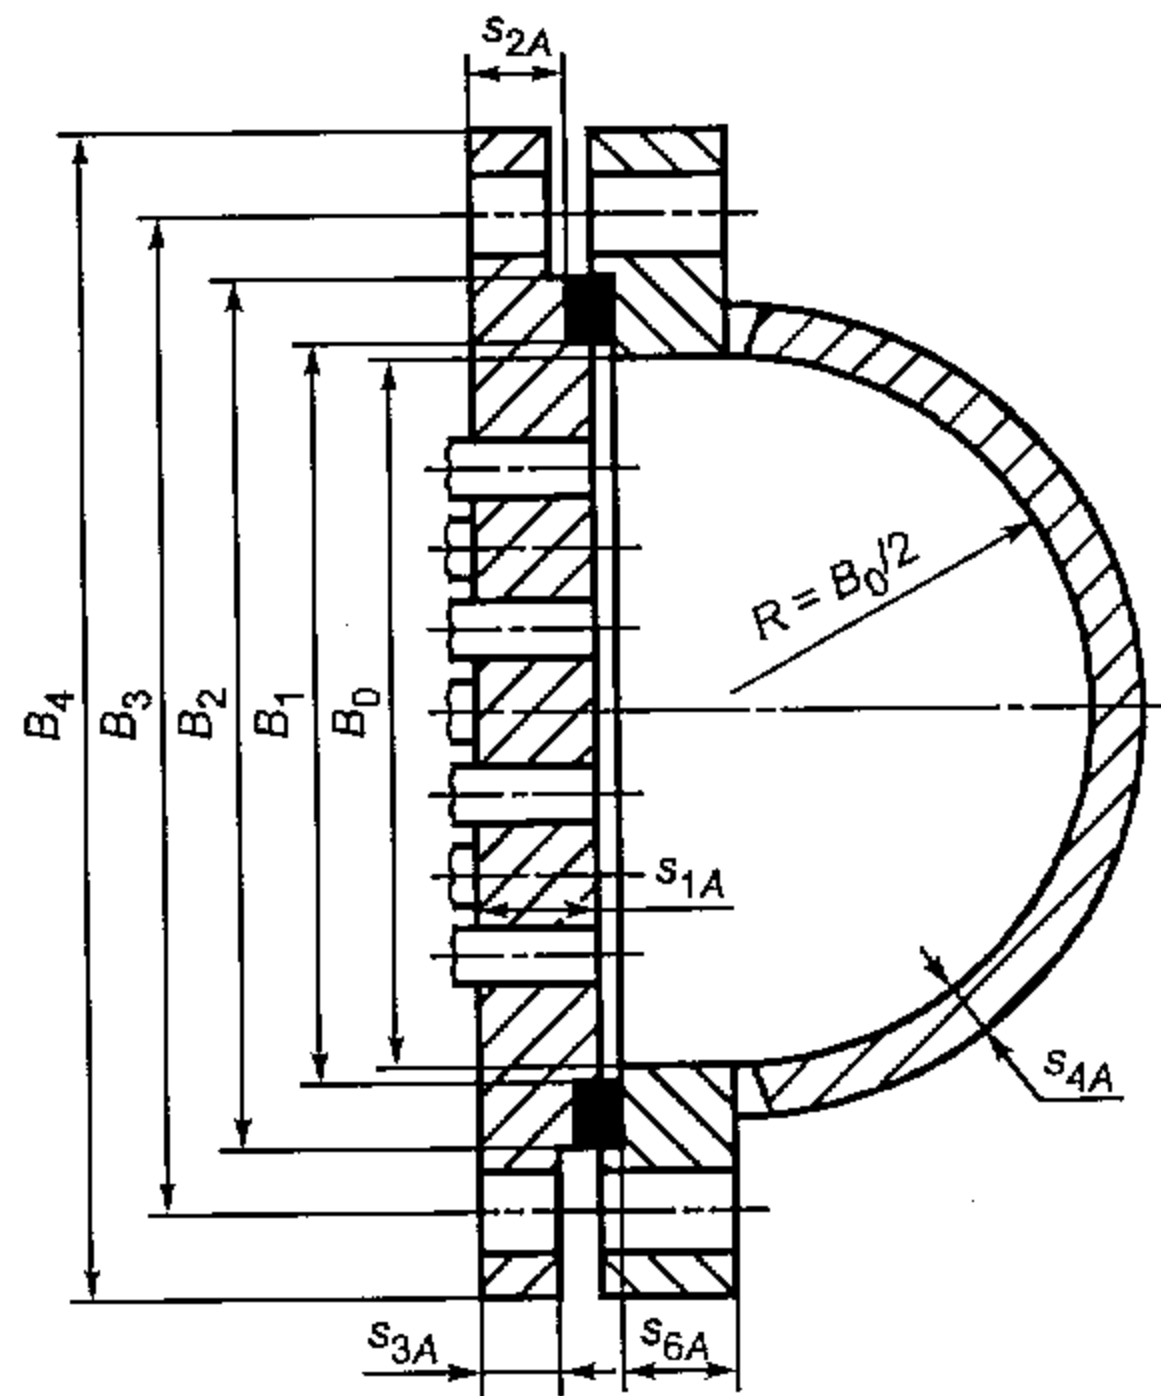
Камера разъемной конструкции со сварной полцилиндрической крышкой
